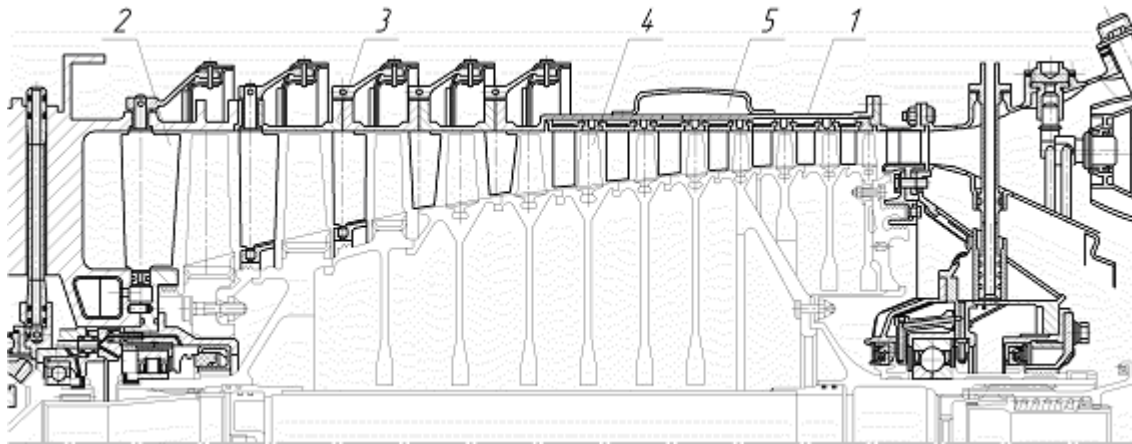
Статор компрессора ТВaД ТВ2-117:
